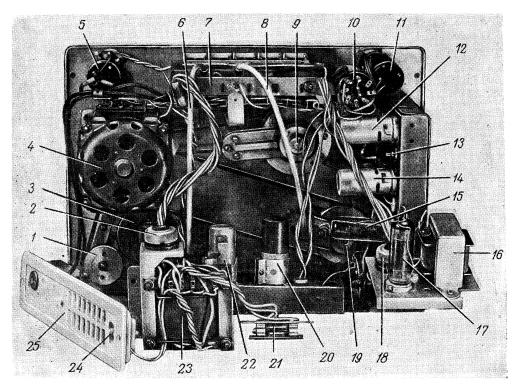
Расположение деталей лентопротяжного механизма и усилителя.
